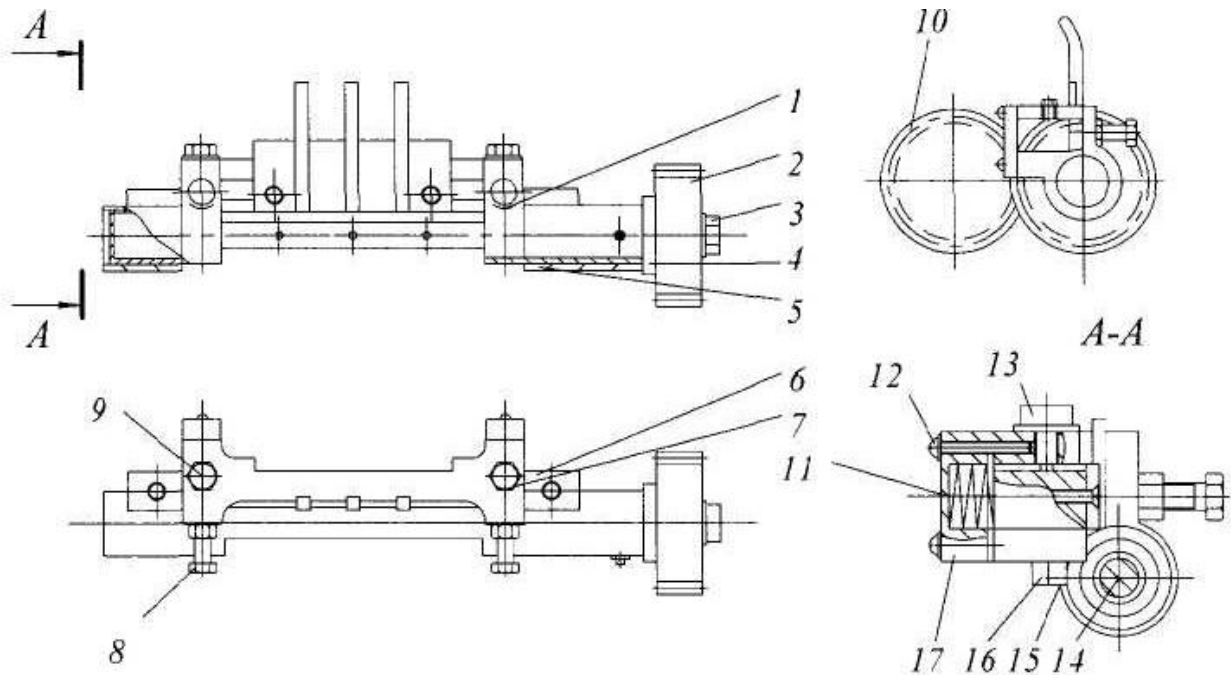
Паперорізальний вузол з гіперболічною симетричною схемою різання:
